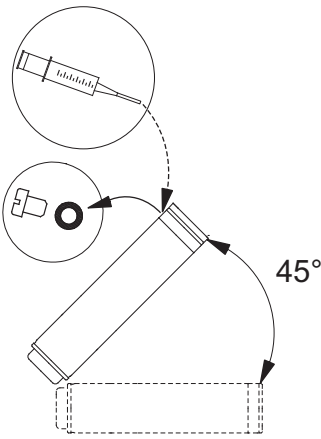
Posición del motor durante el llenado – MS6 y MS 6000
